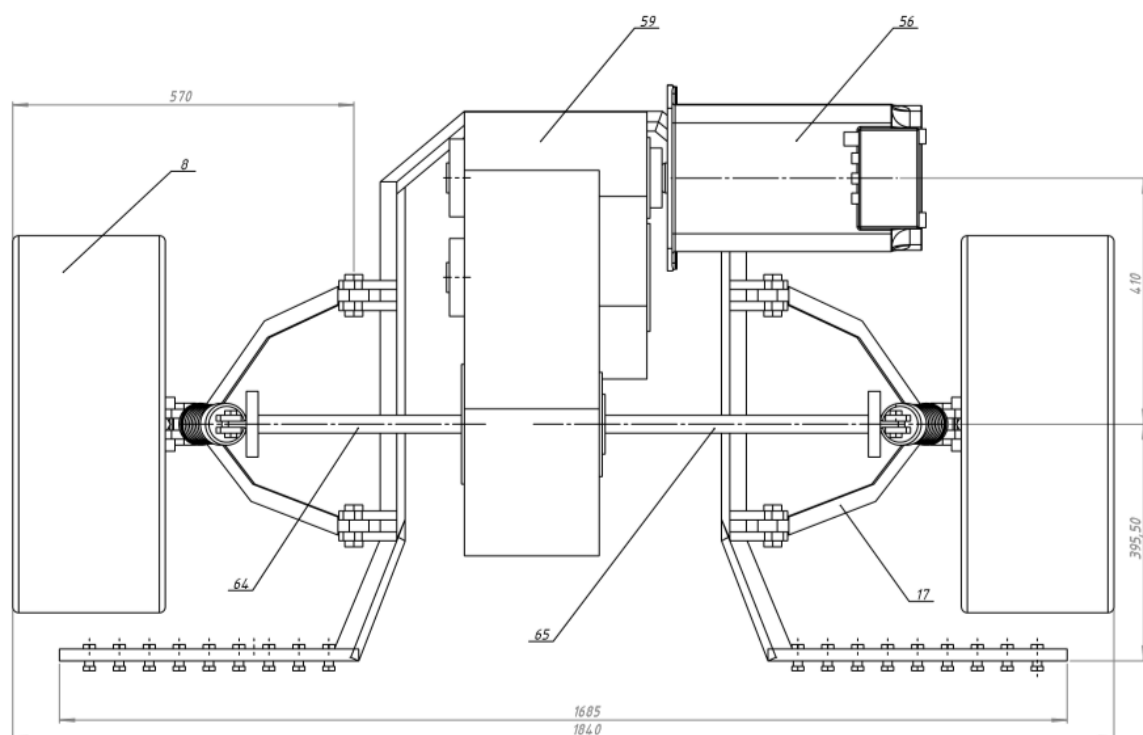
Загальний вигляд заднього приводу(Вид зверху).
